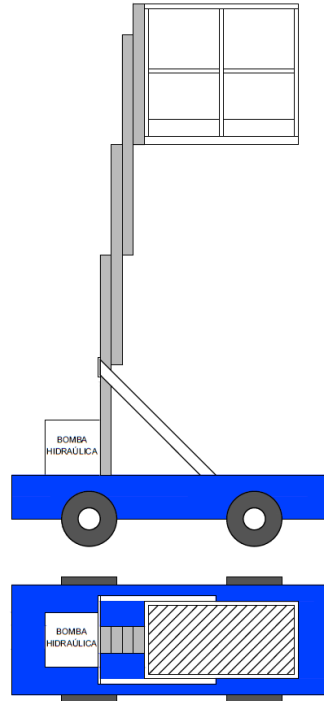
Alternativa de diseño # 1 de elevador de mástil vertical
